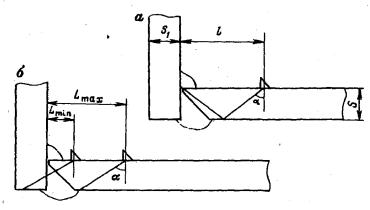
Схемы прозвучивания углового сварного соединения типа У7
